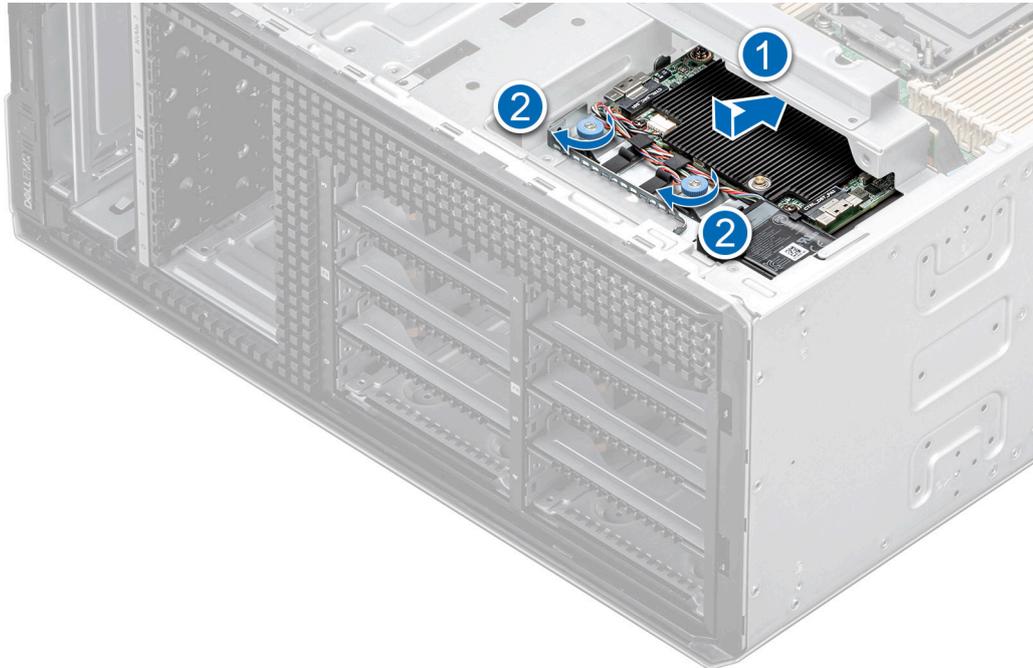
Installieren des PERC-Frontmoduls für die 3,5-Zoll-Laufwerkrückwandplatine.
